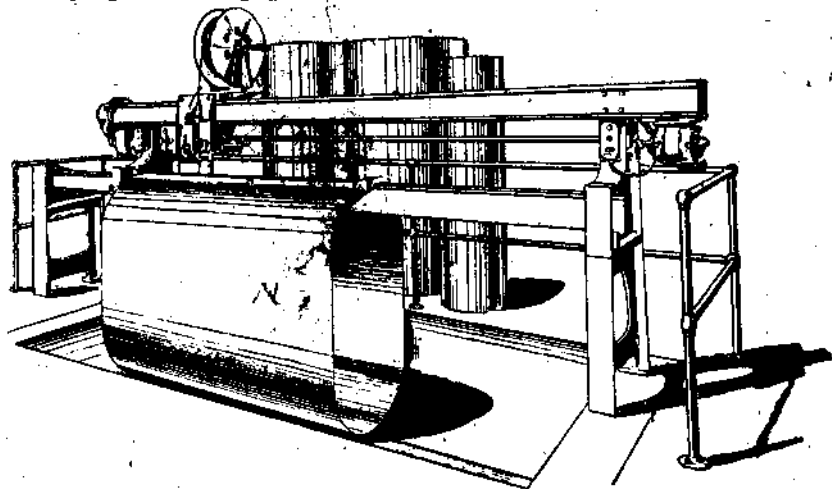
Сварочный автомат для сварки больших резервуаров.
